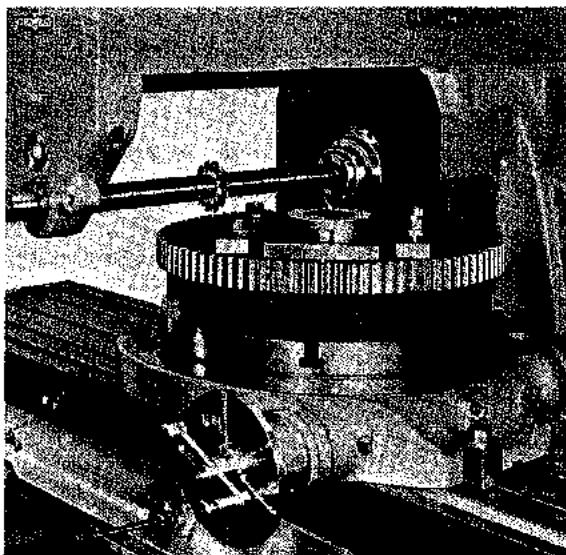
Tallado de dientes de engranaje en una fresadora (Cincinnati Milling Machine Co.)
